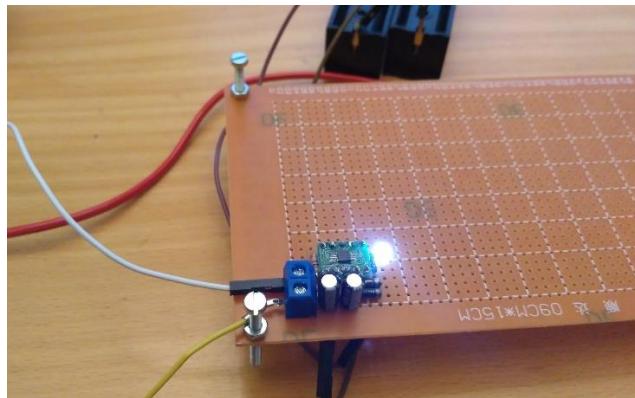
Comprobación de funcionamiento de un chip soldado a la placa PCB.
